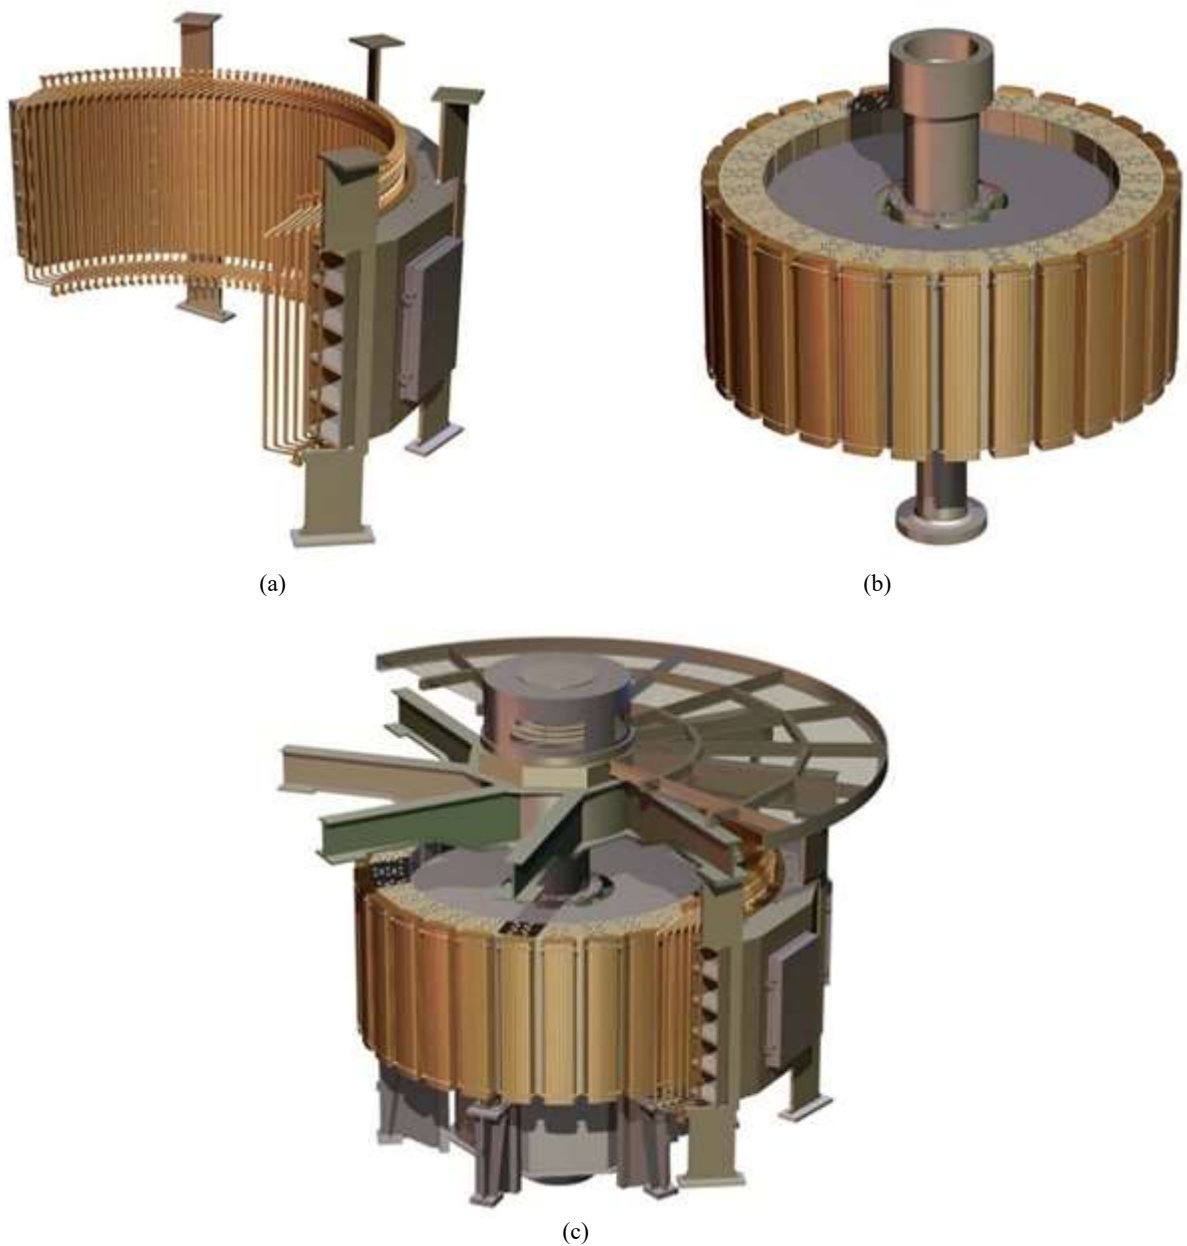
(a) Estator completo: enrolamentos fixados no núcleo; (b) Rotor completo; (c) Máquina completa: Estator + Rotor.
